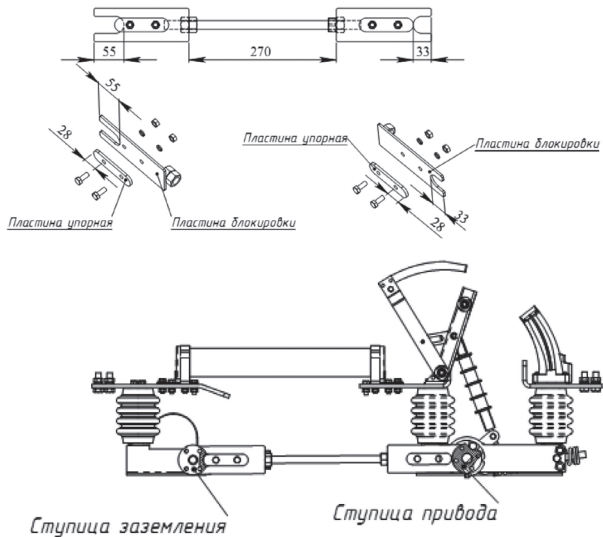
Схема установки блокировки механизма для выключателей с плавкими предохранителями
